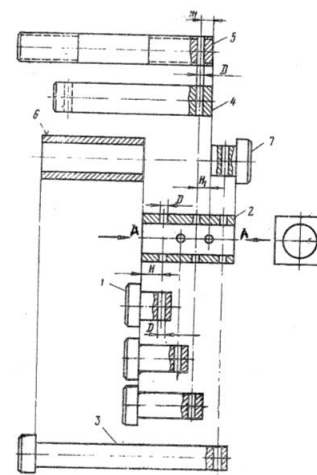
Схема сверления отверстий в осях и шпильках под шплинт с применением универсального кондуктора
